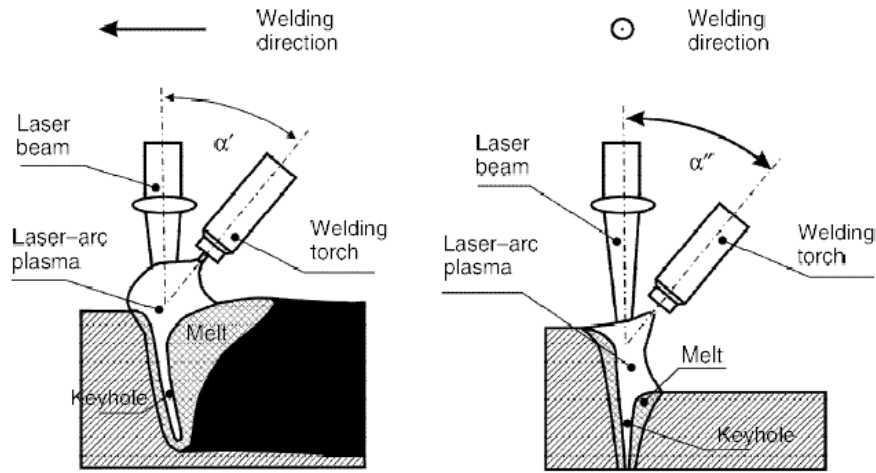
Representação esquemática de operações com o ponto comum de um processo de soldadura híbrido laser-arco, [8].
